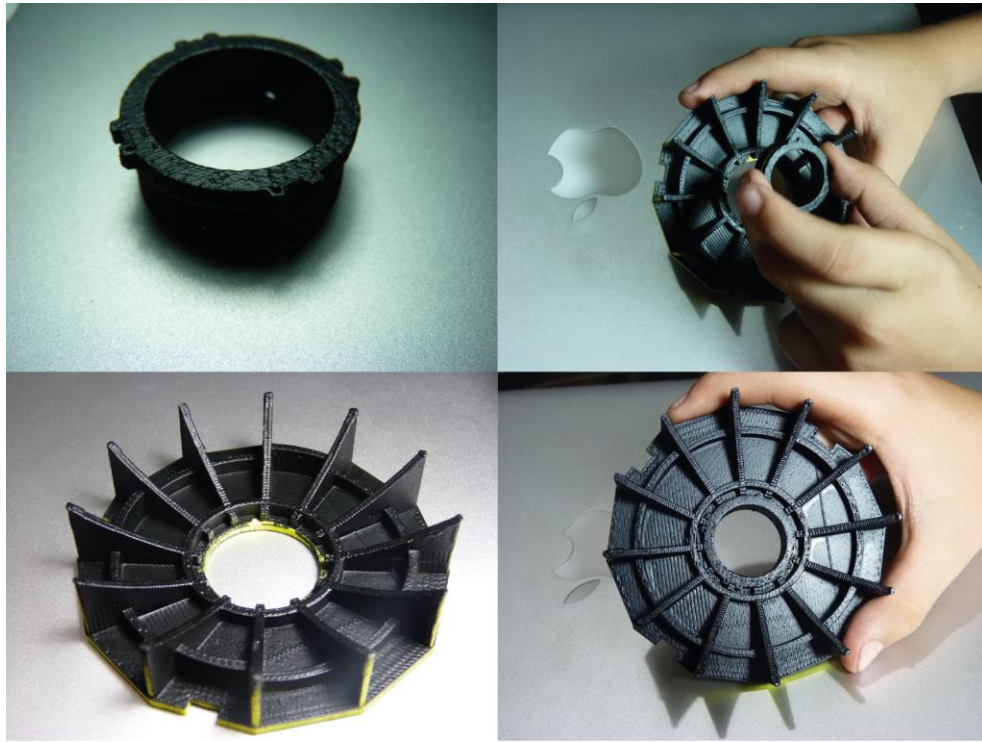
Ensamblaje de estructura reflector. Fuente: Autora.
